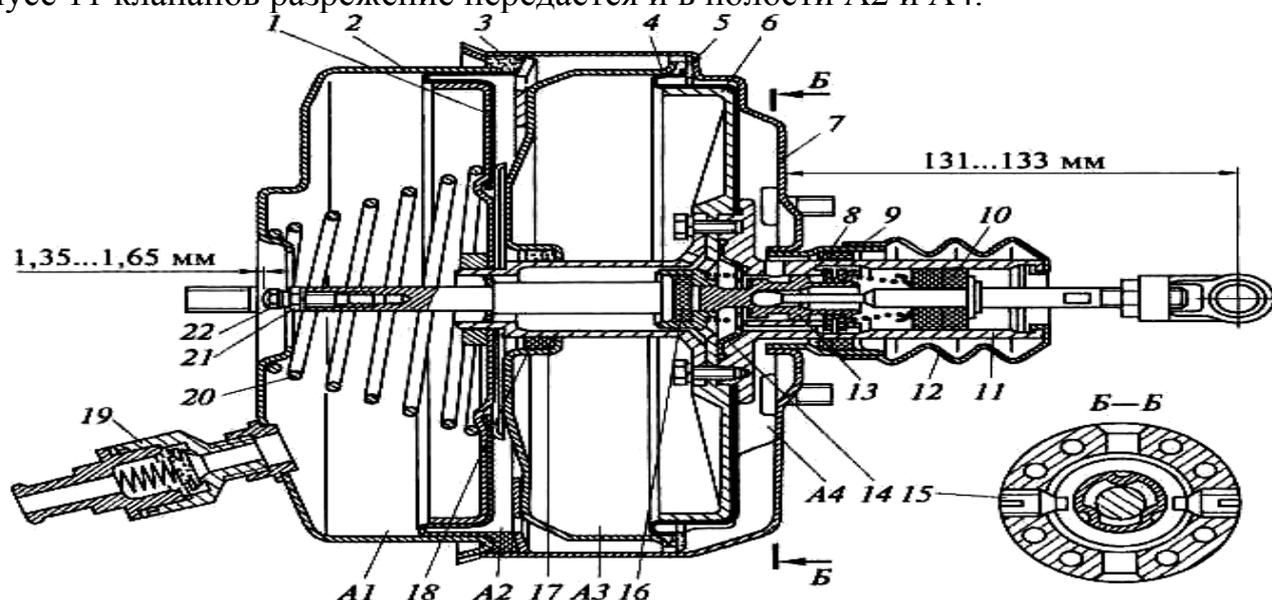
Вакуумный усилитель тормозного привода: 1, 6, 13 — поршни; 2 — крышка корпуса; 3, 4 — диафрагмы; 5 — упорное кольцо; 7 — корпус усилителя; 8, 17 — направляющие кольца; 9, 18 — уплотнительные манжеты; 10 — фильтр; 11 — корпус клапанов; 12 — защитный резиновый чехол; 14 — диафрагма клапанов; 15 — винт; 16 — реактивная шайба; 19 — обратный клапан; 20 — пружина; 21 — контргайка; 22 — регулировочный болт; А1— А4 — полости вакуумного усилителя
